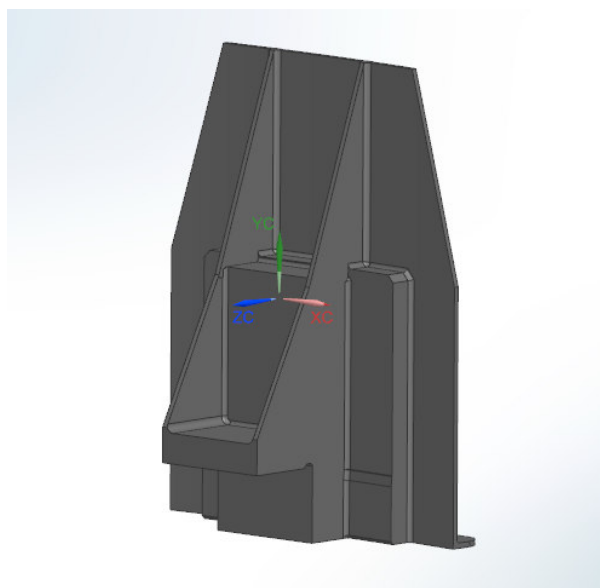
Измененная конструкция заготовки для черновых и получистовых проходов
